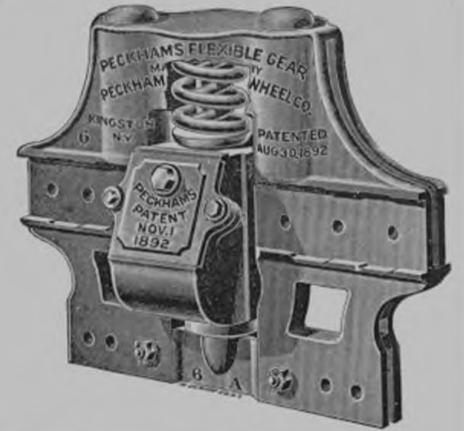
PLAQUE DE GARDE ET BOITE DU CHASSIS PECKHAM
